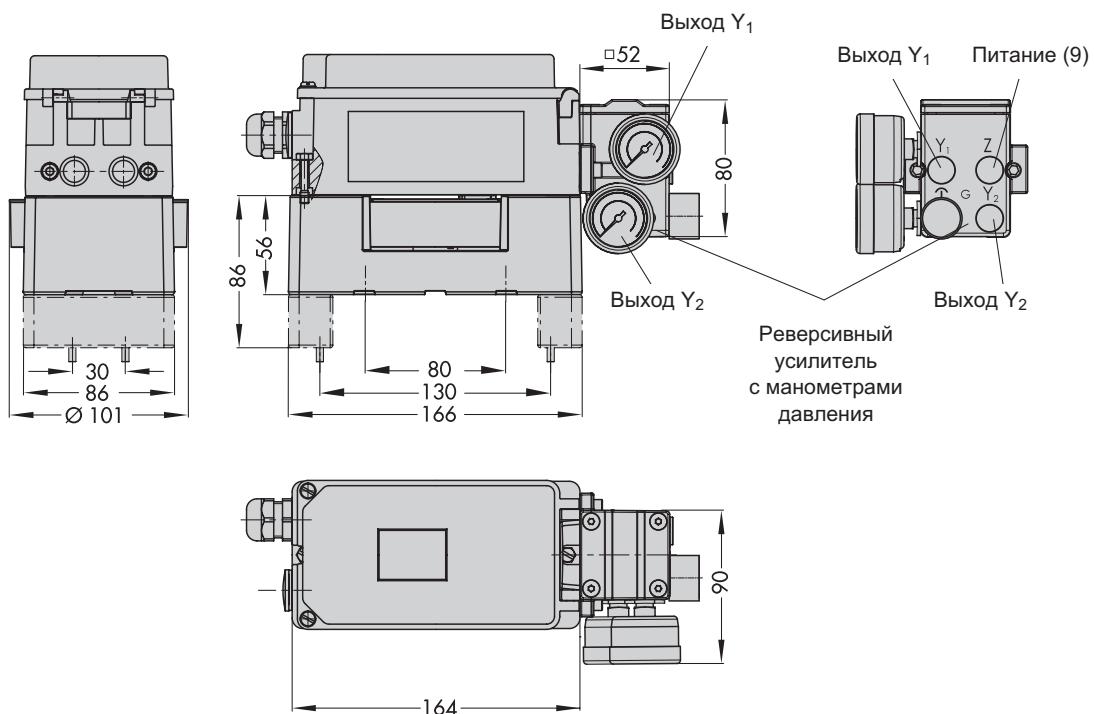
· Размерный рисунок Реверсивного усилителя Типа 3710, монтируется на Позиционер Типа 3730
